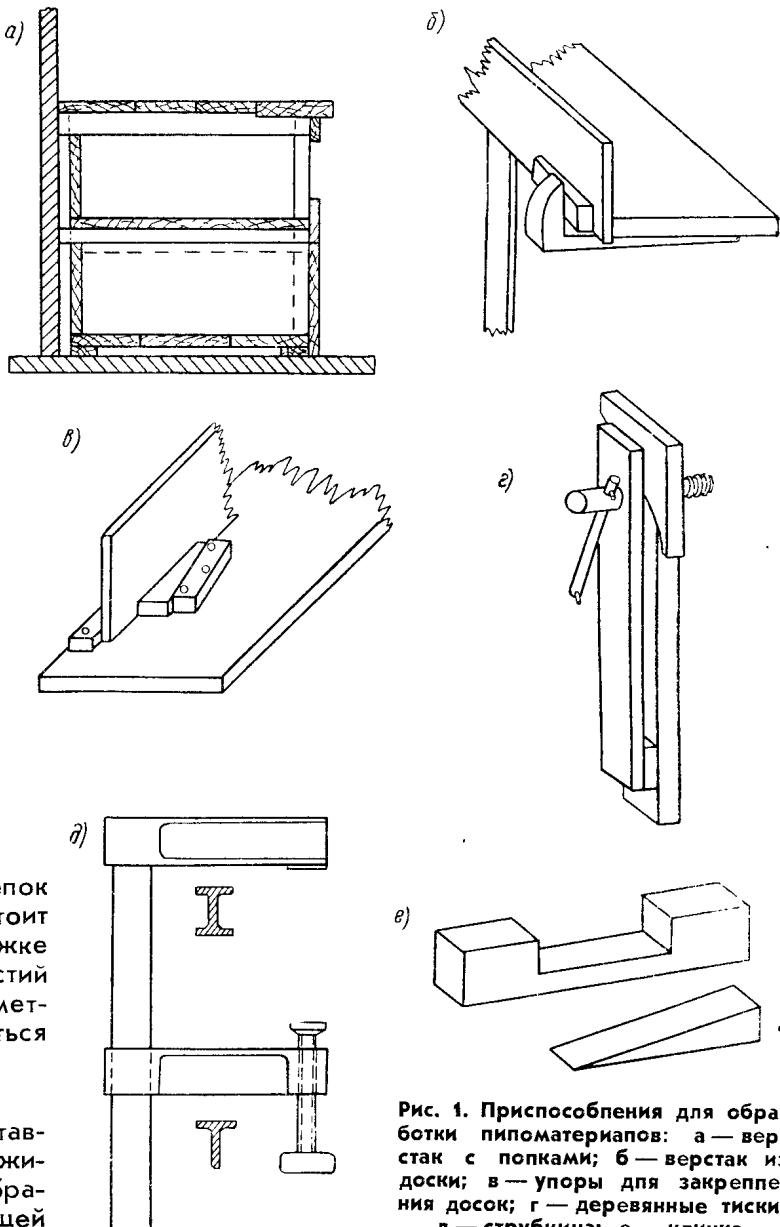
Приспособления для обработки пиломатериалов: а — верстак с попками; б — верстак из доски; в — упоры для закрепления досок; г — деревянные тиски; д — струбцина; е — цвinka.
